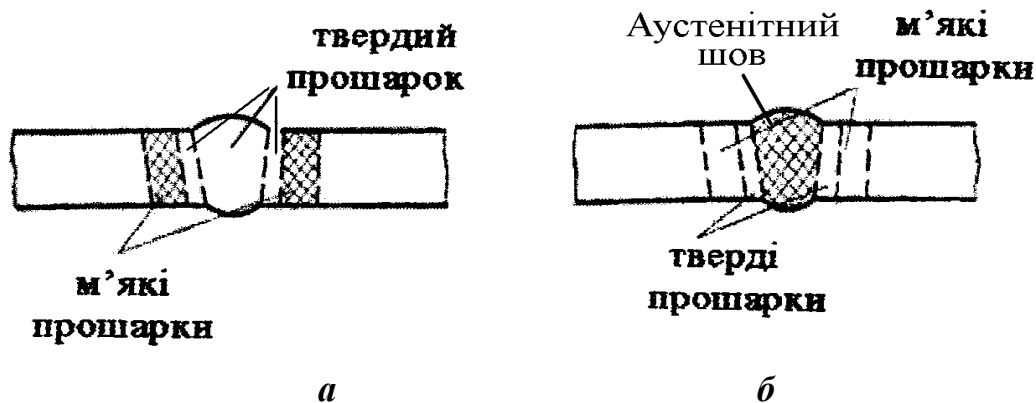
Тверді і м'які прошарки в зварних з'єднаннях
